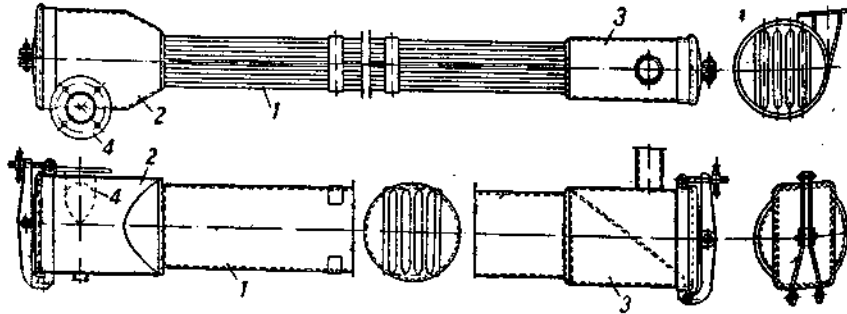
Холодильник: 1—плоские трубы, 2—задняя сборная коробка, 3—передняя сборная коробка, 4—патрубок с фланцем
